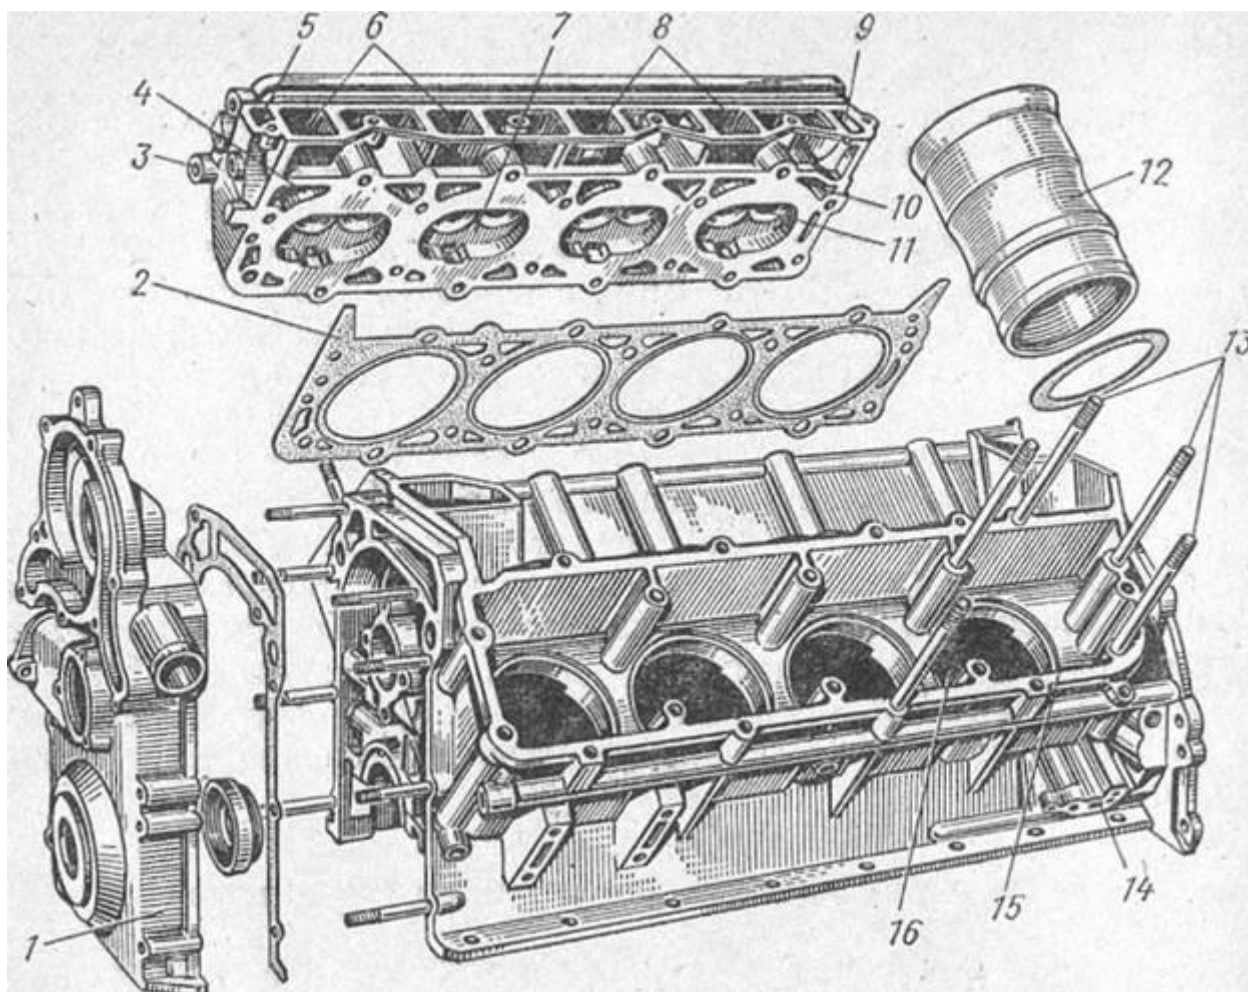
Блок цилиндров, гильза, крышка распределительных шестерен и головка блока двигателя ЗМЗ-53
